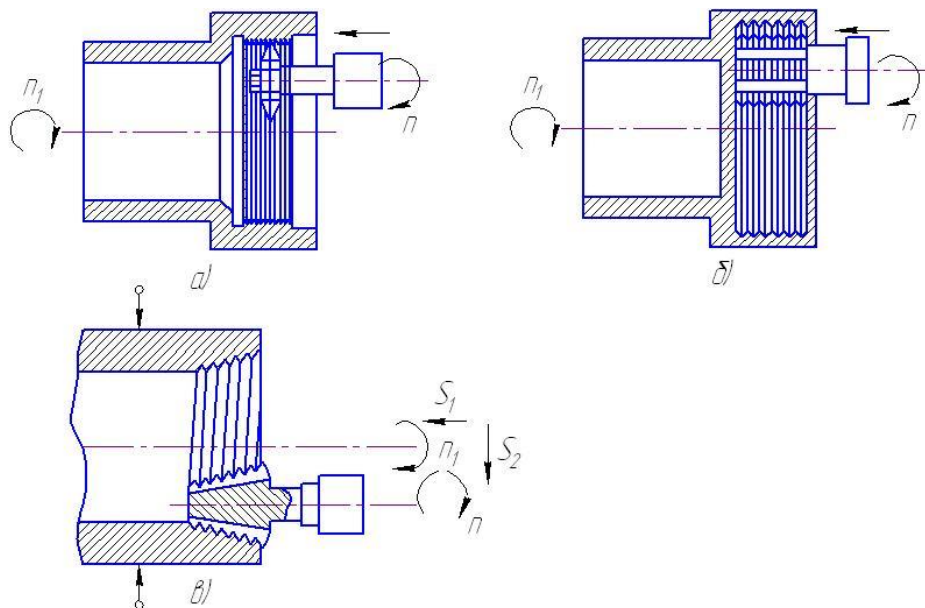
Фрезерование резьбы: а) дисковой фрезой; б) групповой фрезой; в) групповой фрезой с планетарным движением инструмента
